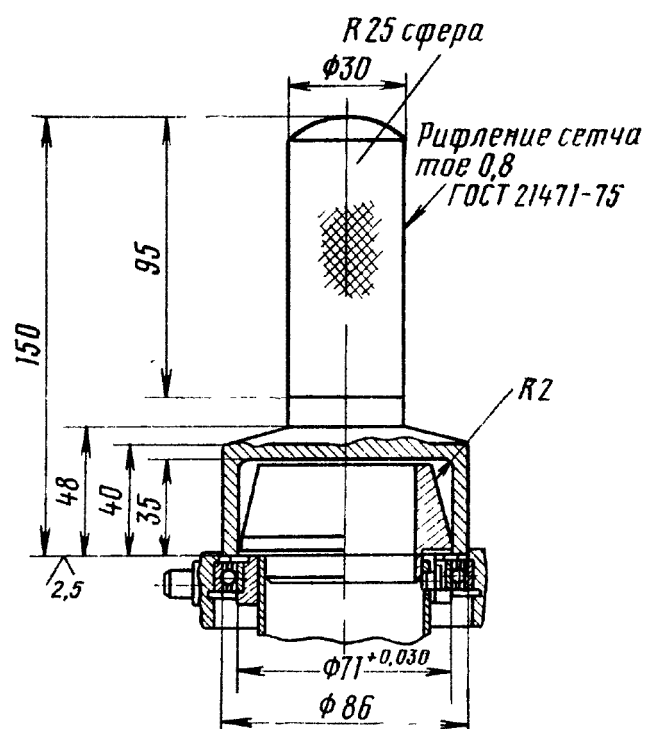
Оправка для установки стопорного кольца в обойму механизма блокировки дифференциала заднего моста
